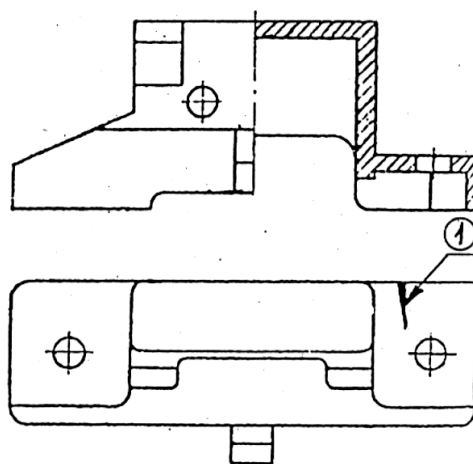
Лапа крепления асинхронного двигателя
